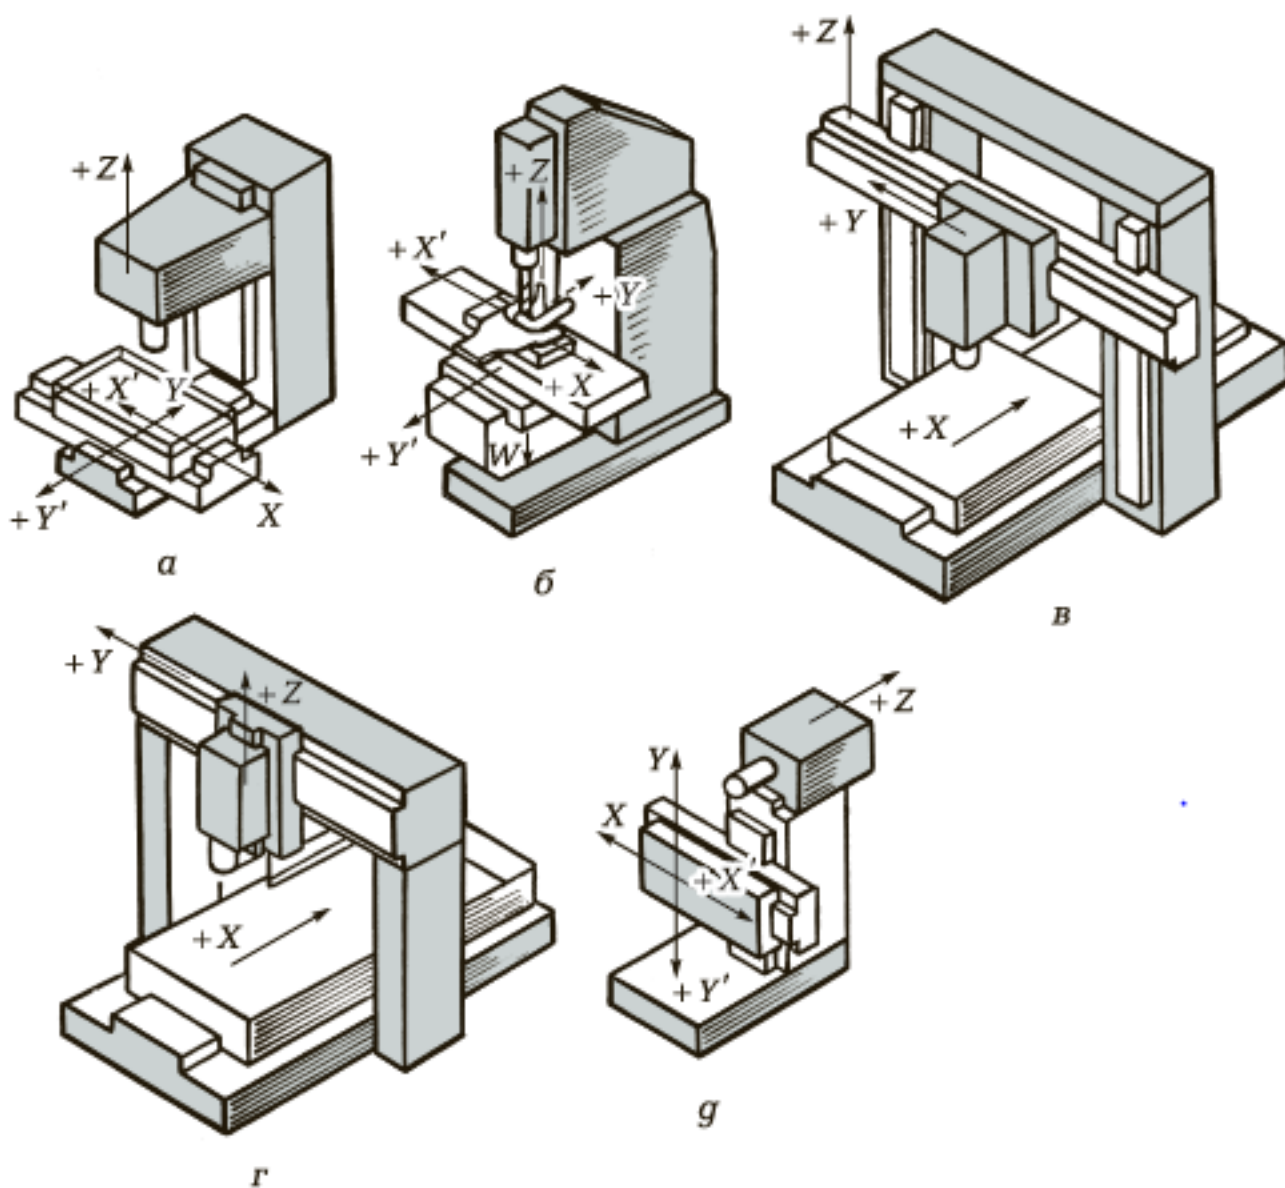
Компонровка фрезерных станков с ЧПУ:
